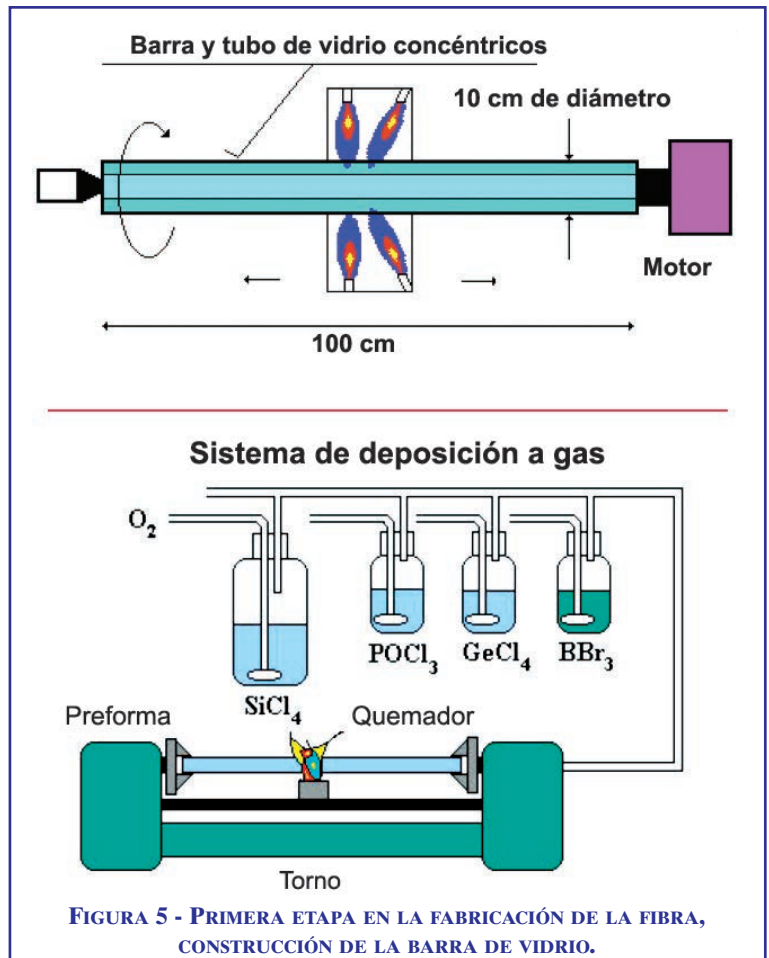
PRIMERA ETAPA EN LA FABRICACIÓN DE LA FIBRA, CONSTRUCCIÓN DE LA BARRA DE VIDRIO.
